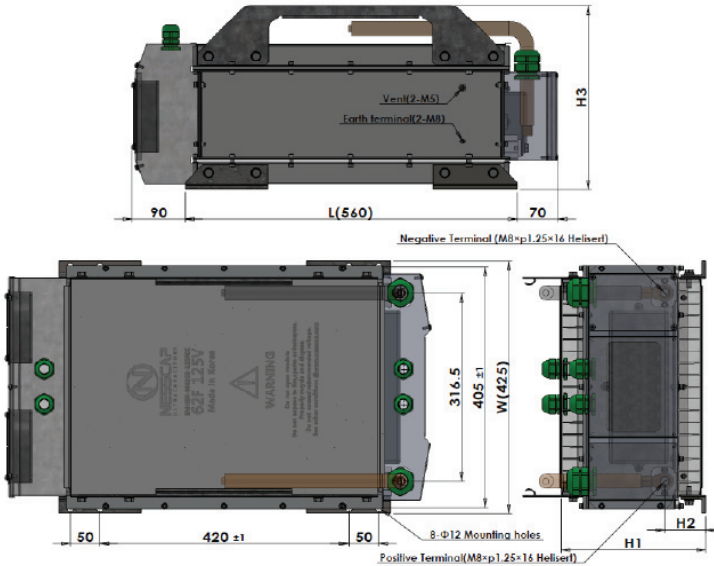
Dimensões físicas do módulo 125 V 62 F.
